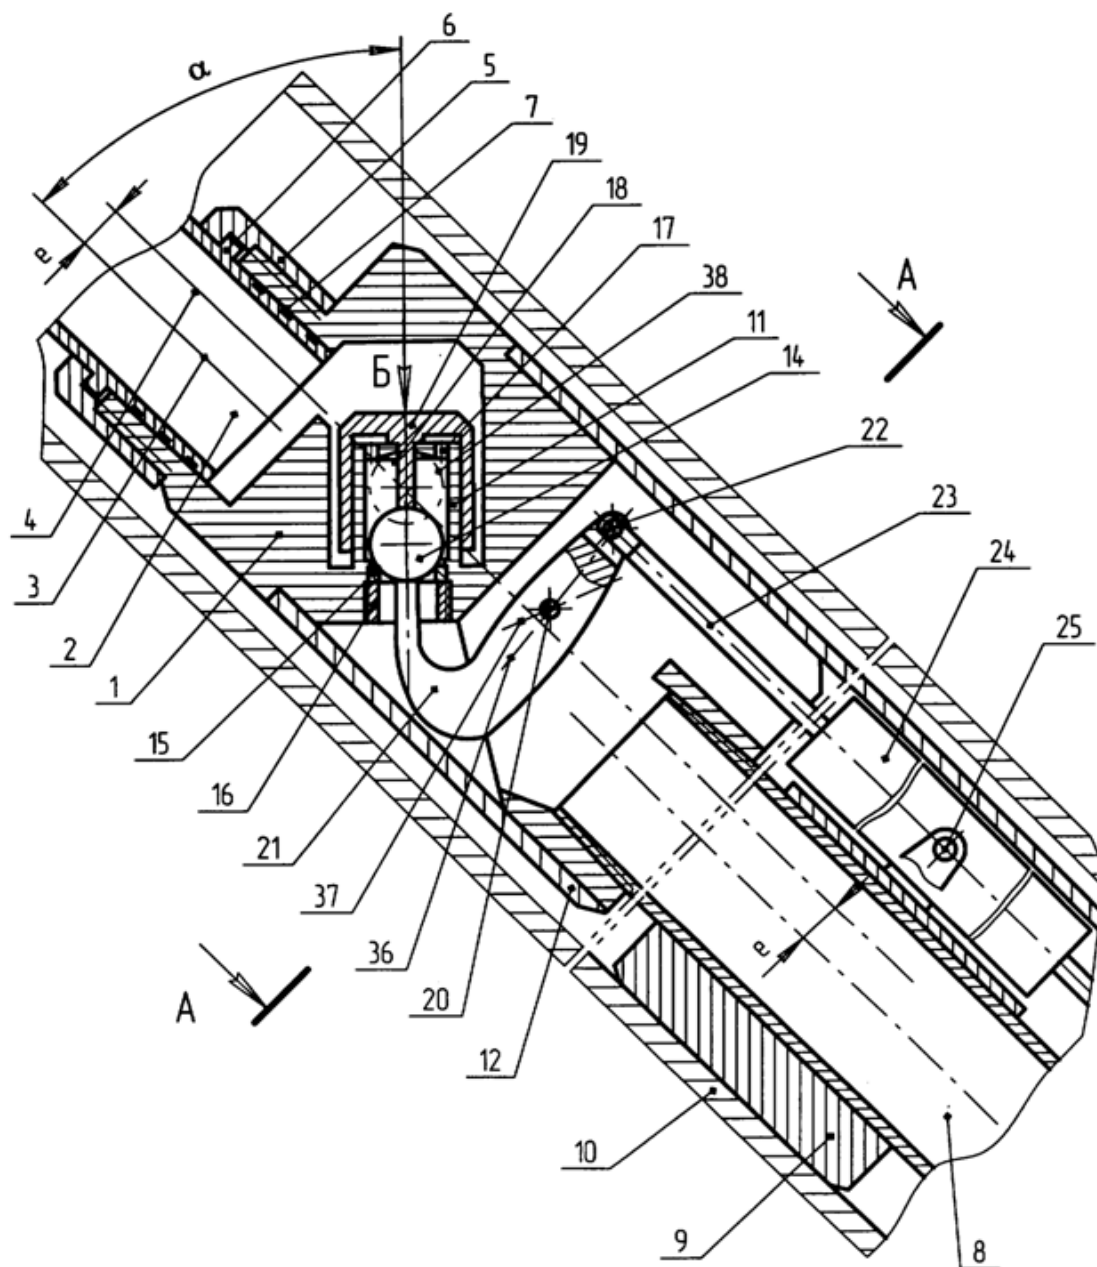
Самоустанавливающийся управляемый всасывающий клапан
